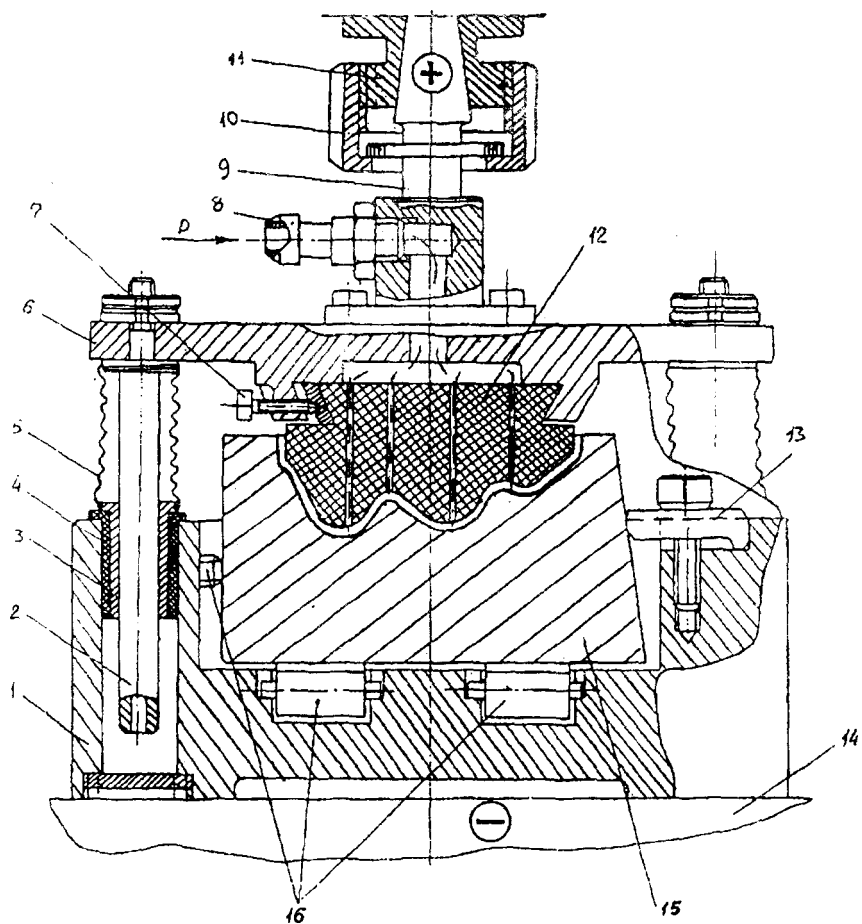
Приспособление для электроэрозионного формообразования сложной поверхности гравюры ковочного штампа
